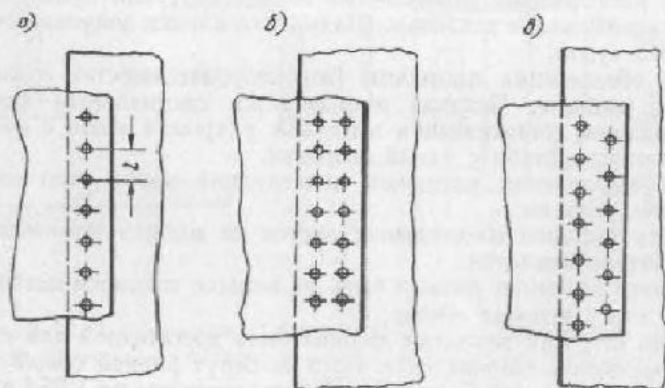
Типы заклепочных швов: *a* — цепной однорядный; *б* — цепной двухрядный; *в* — шахматный двухрядный.
